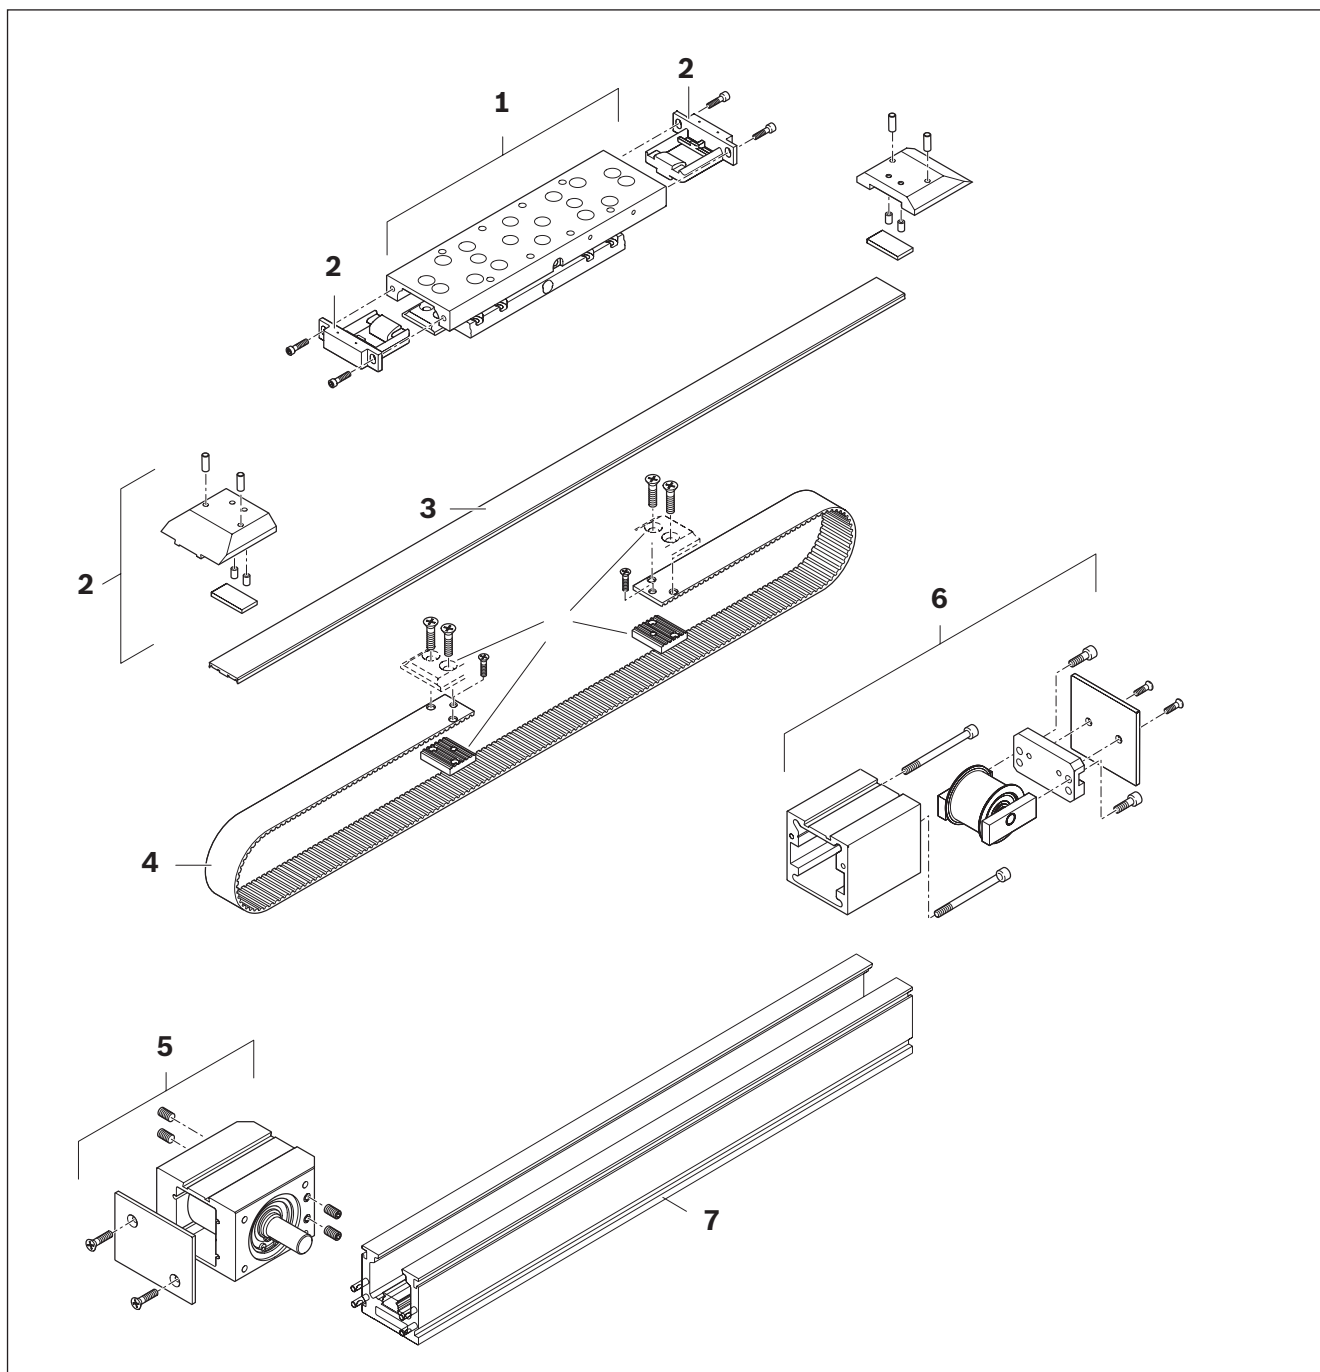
Vue d'ensemble MKR-040-NN-3
